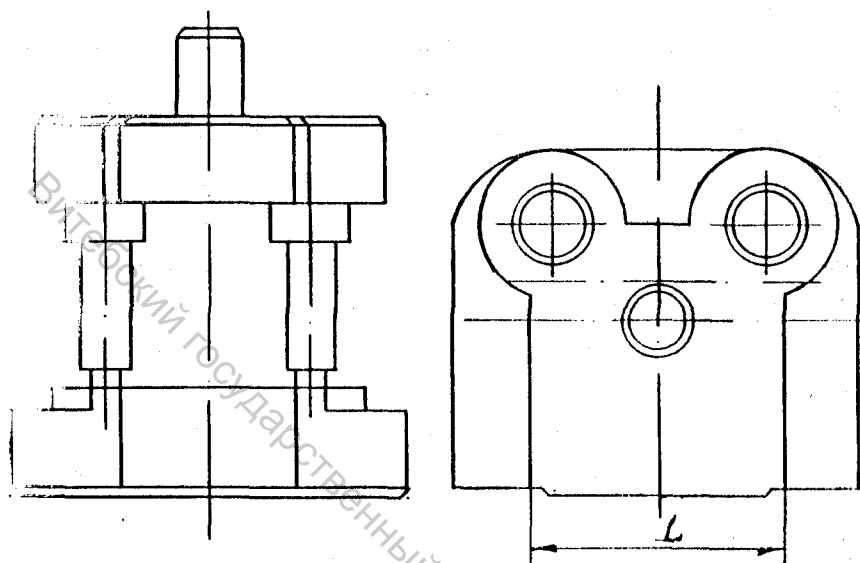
Стандартный блок с задним расположением направляющих колонок.
